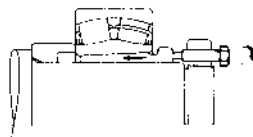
Посадка подшипника на запрессовываемой втулке
